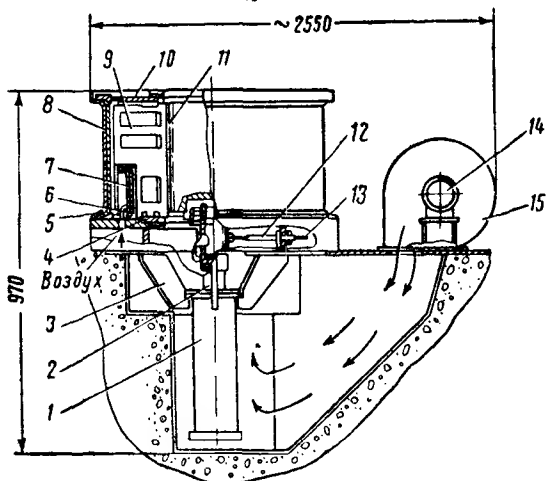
Установка для осадки обмотки якоря электродвигателя типа ЭДТ-200:
